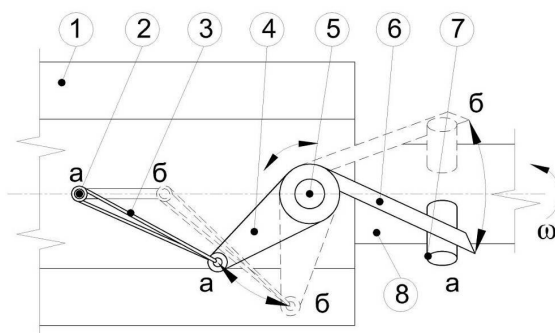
Механізм переривчастого поступально-зворотного руху для автоматичної подачі зарядів вибухової речовини до продувного каналу: 1 – корпус вертлюга; 2 – затвор; 3 – ланцюг з'єднувальний; 4 – важіль тяговий; 5 – стрижень механізму; 6 – важіль контактний; 7 – палець ведучої ланки; 8 – ведуча ланка
